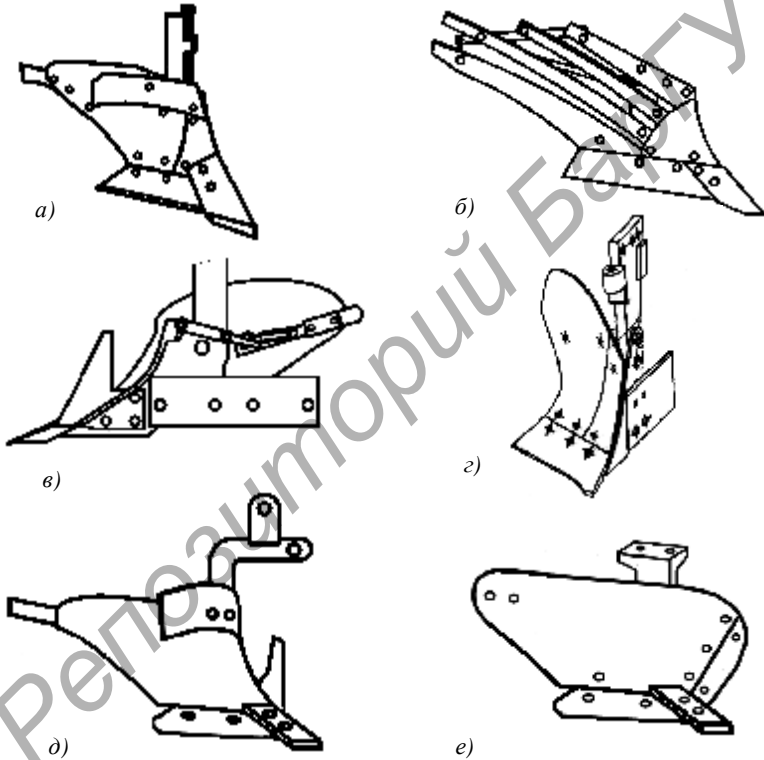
Основные типы отвальных плужных корпусов:
